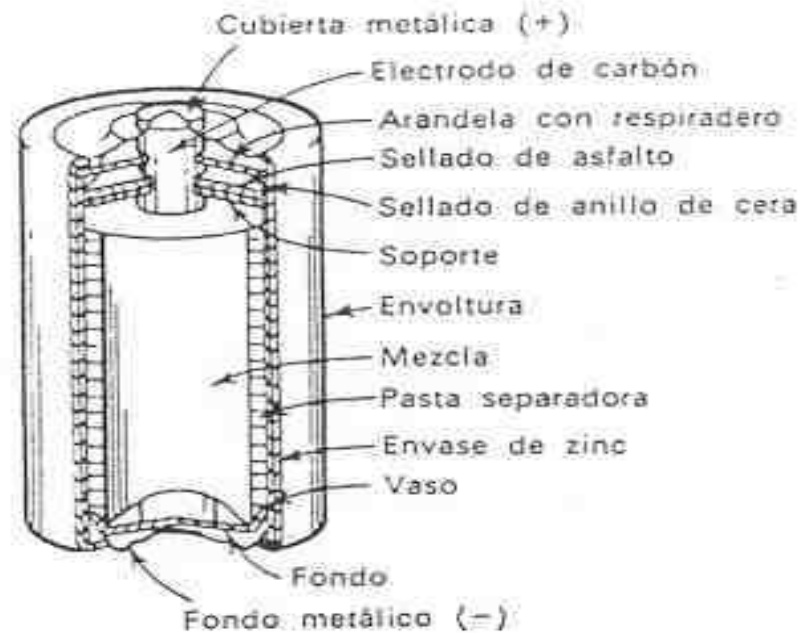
Sección de una pila cilíndrica Leclanché.
